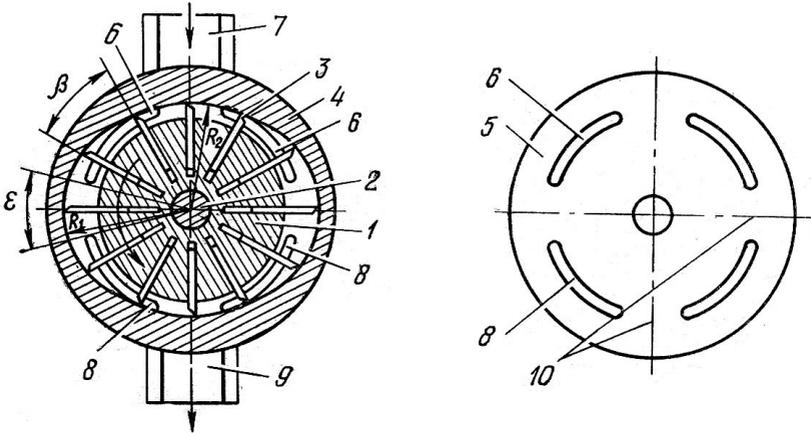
Роторно-пластинчатый насос двукратного действия: 1- ротор; 2- вал; 3- пластины; 4- корпус (статор); 5- распределитель; 6- окно гидролинии всасывания- 7; 8- окно гидролинии нагнетания- 9; 10 - перемычка
